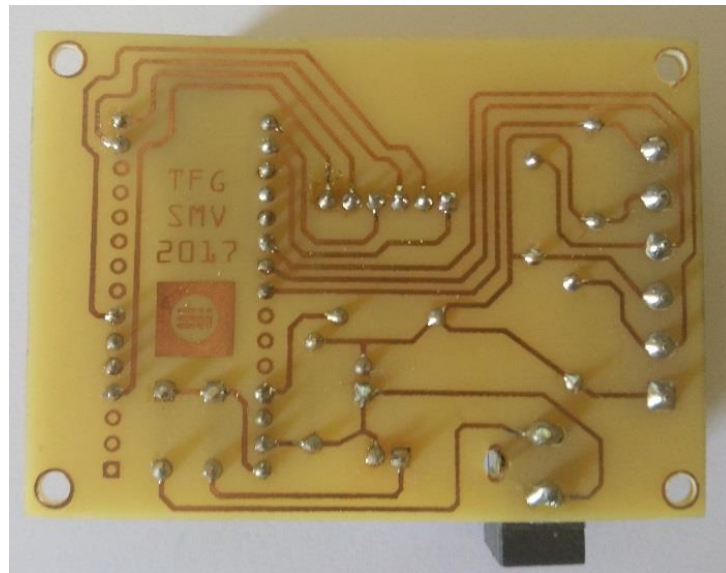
Placa vista desde la parte inferior con los componentes soldados.
